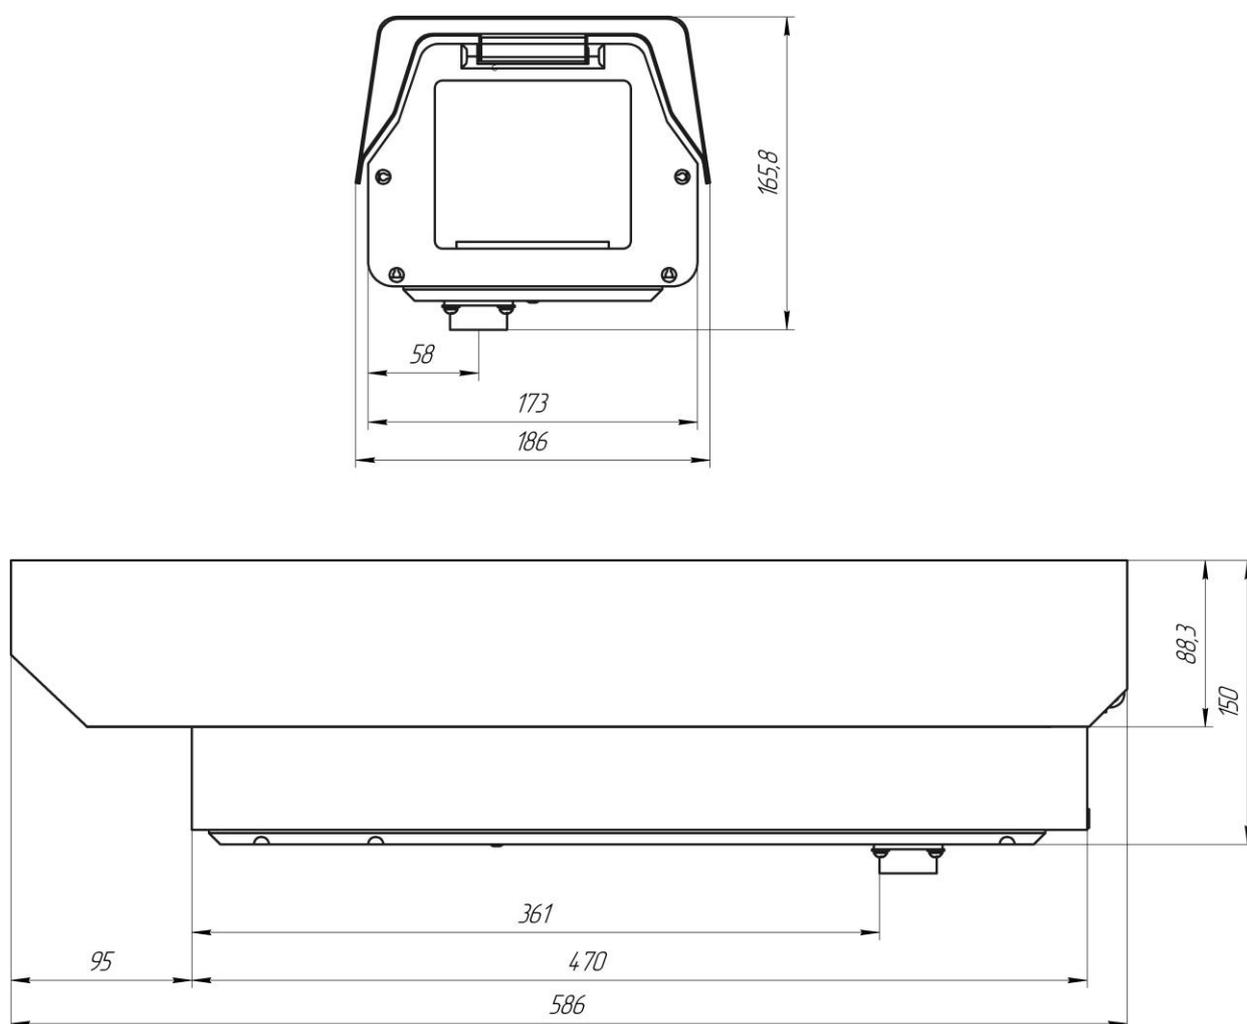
Габаритные размеры видеокамеры SDP-8083
